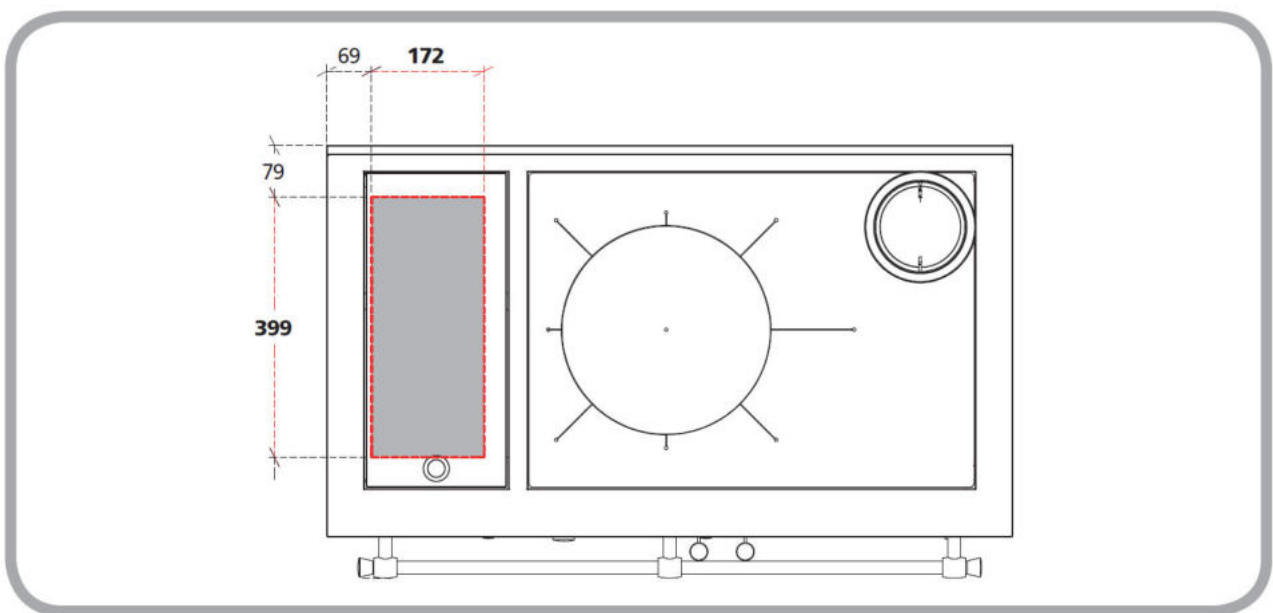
Posizione del foro inferiore per il passaggio delle tubazioni
